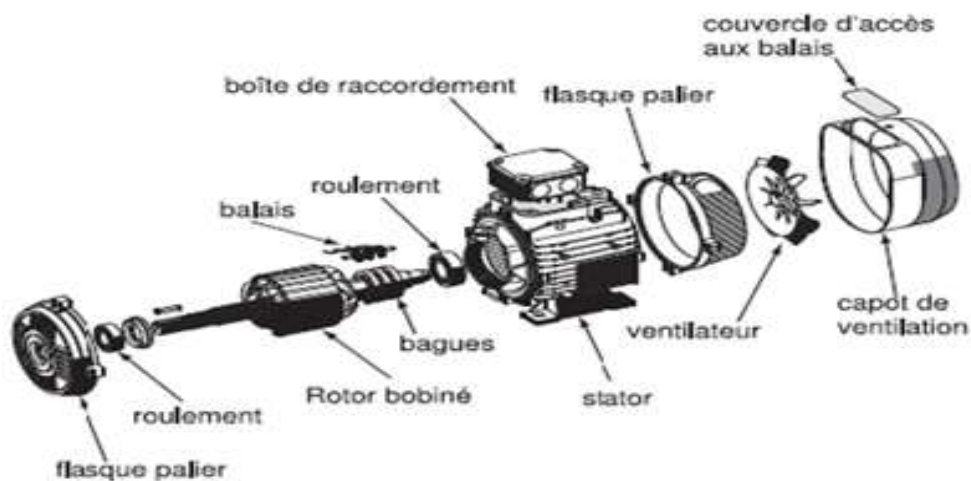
Vue éclatée d'un moteur asynchrone à rotor bobiné
